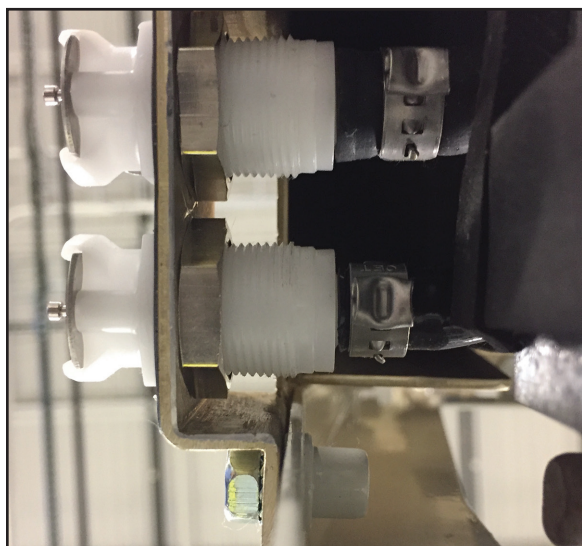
Arrière des robinets de vidange (étape 5)
